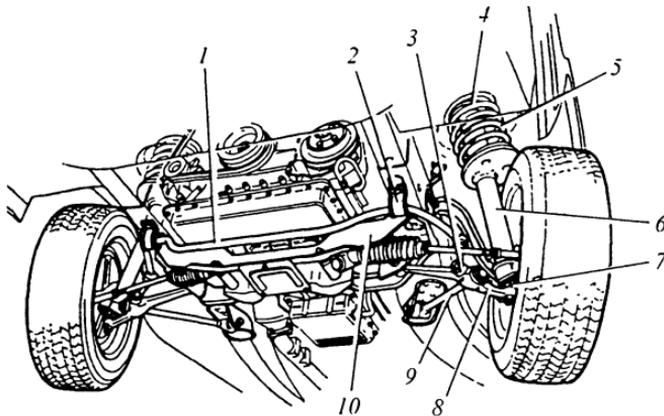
Передняя подвеска: 1 — стабилизатор поперечной устойчивости; 2 — кронштейн стабилизатора; 3 — стойка стабилизатора; 4 — верхнее крепление стойки амортизатора; 5 — пружина; 6 — трубка стойки; 7 — шаровый шарнир управляющего рычага; 8 — управляющий рычаг; 9 — толкающая штанга; 10 — передняя поперечина
